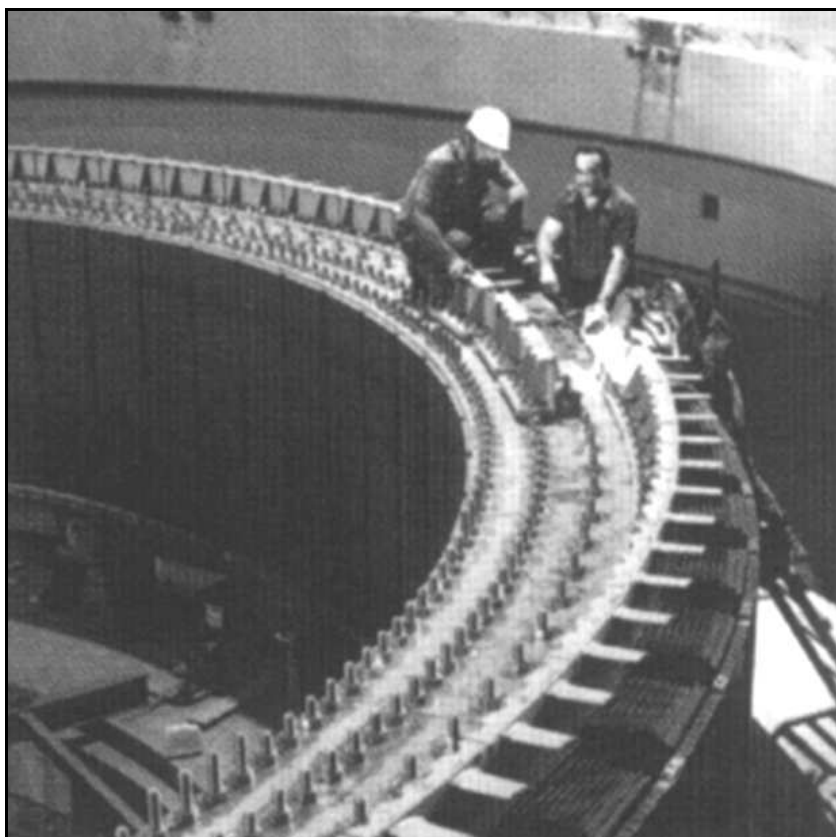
Vista da colocação das turbinas (FONTE: FURNAS).
